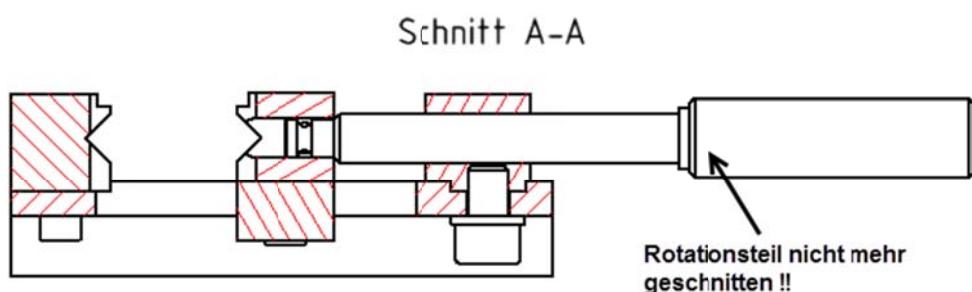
Bauteil nicht mehr geschnitten dargestellt
